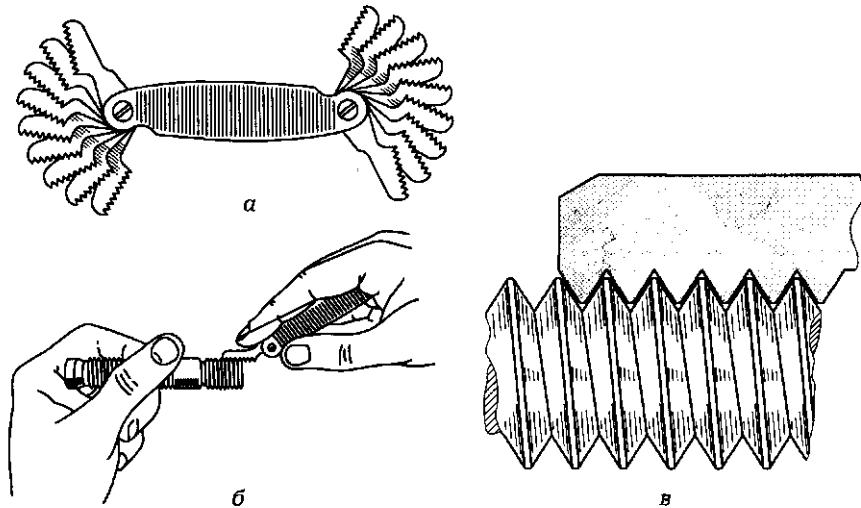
Резьбовые шаблоны (резьбомеры):
